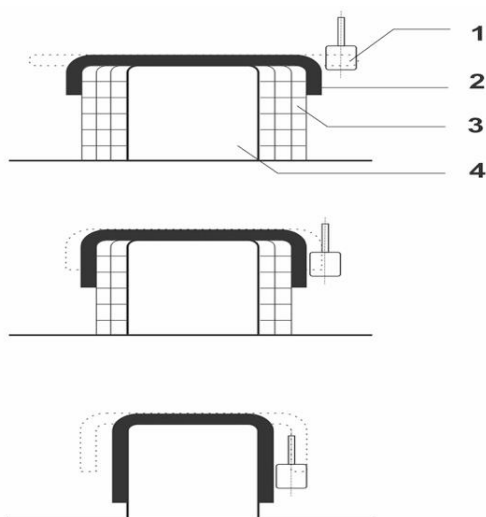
Схема формообразования на фрезерном станке с ЧПУ при помощи специальных цилиндров (прижим заготовки к оправке условно не показан):
